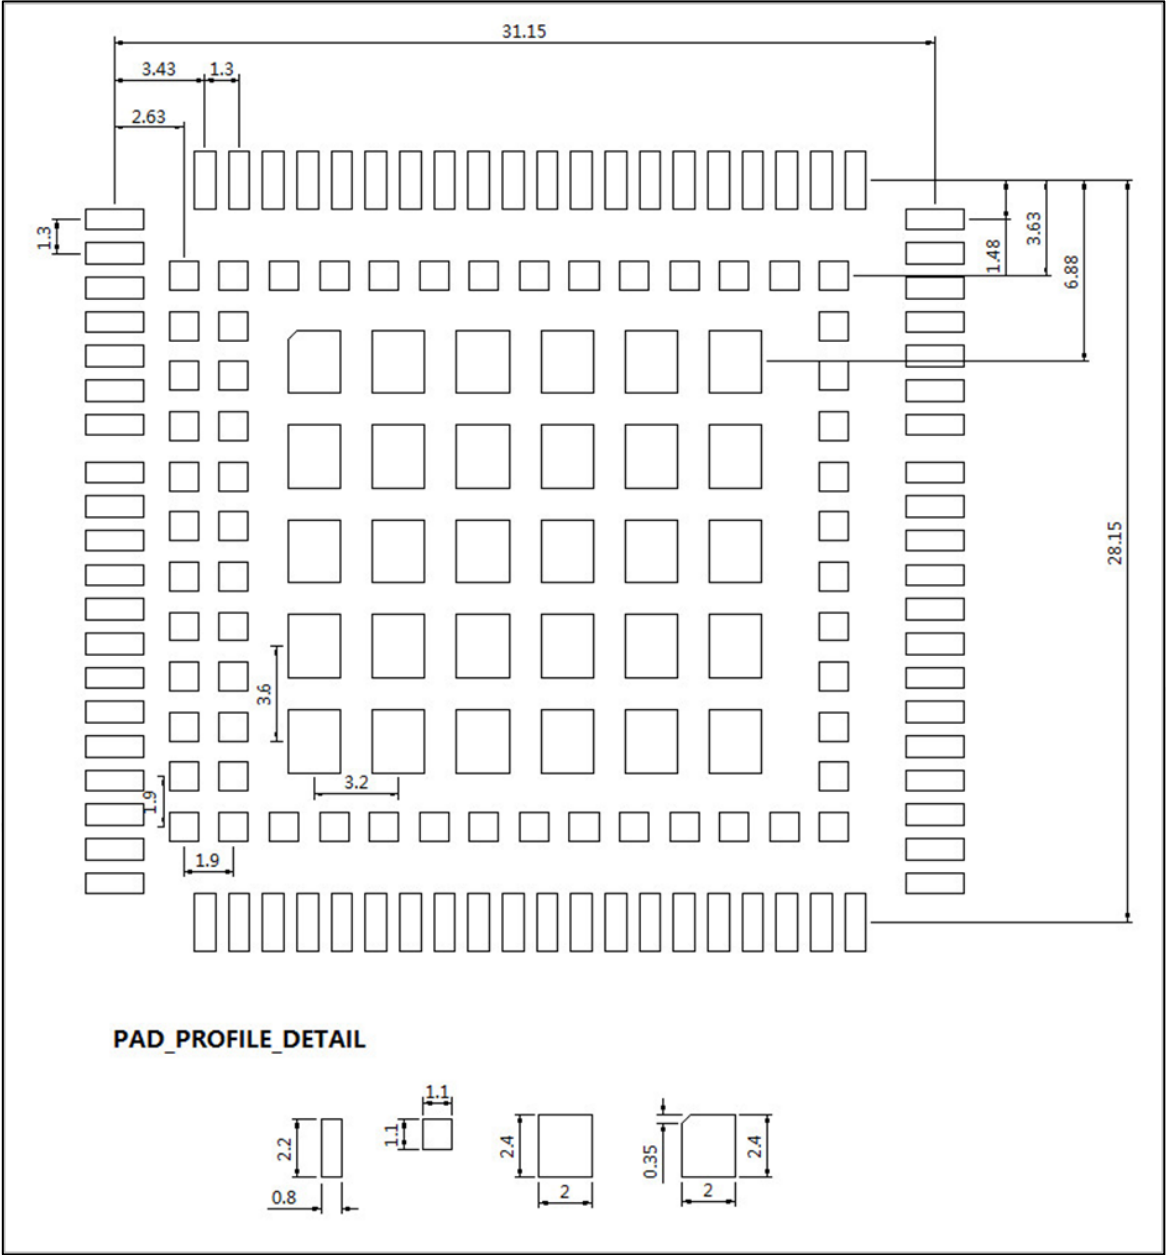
PCB 焊盘兼容尺寸 (单位: mm)
